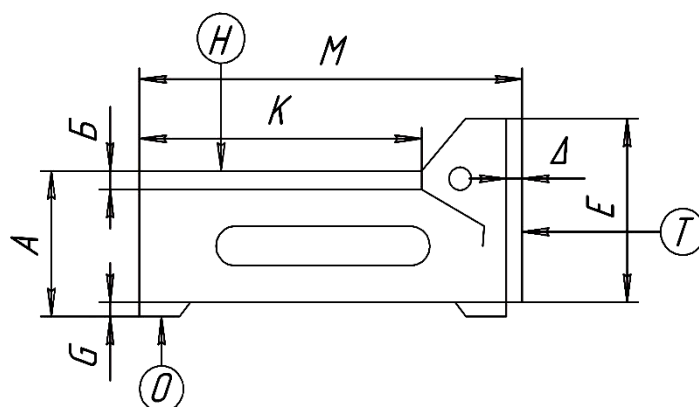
Эскиз заготовки разъемной горизонтальной части станины вертикально-фрезерного станка
